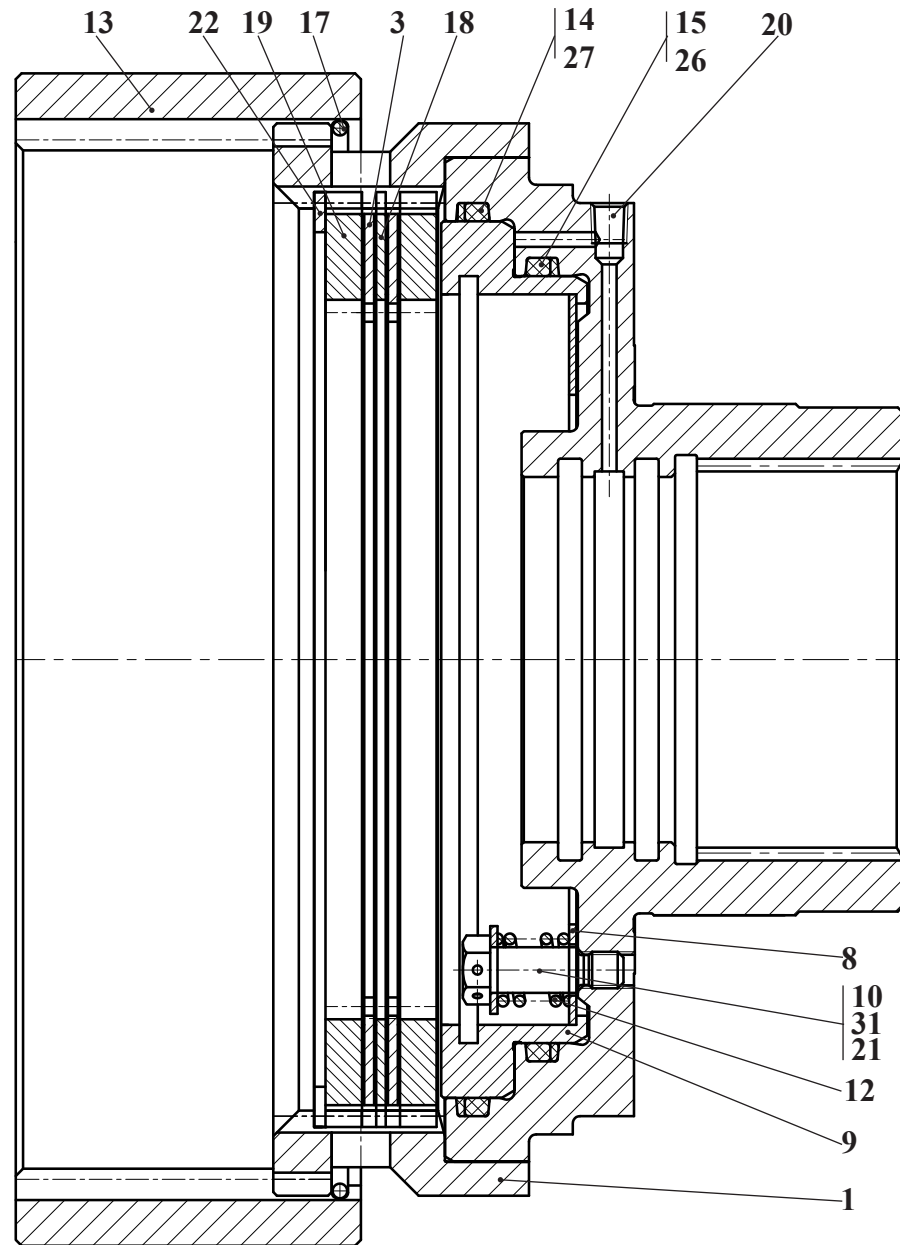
У2210.20Н-2-03.100-03-Б	Тормоз колесный
